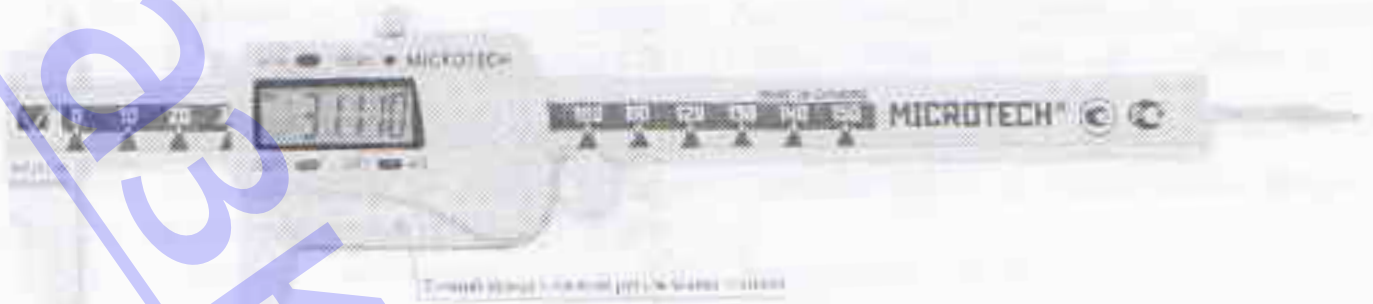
Штангенциркуль ШЦЦПУ-1
